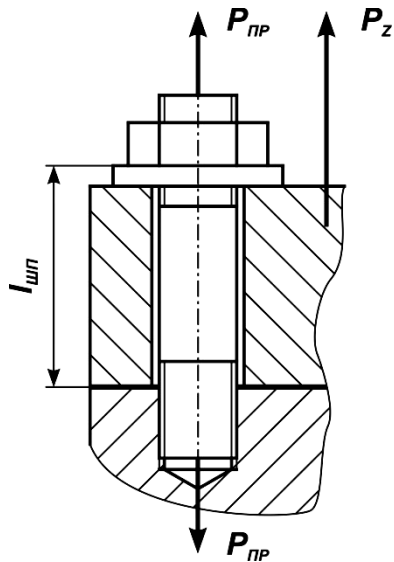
Розрахункова схема елементів з'єднання корпусних деталей.
